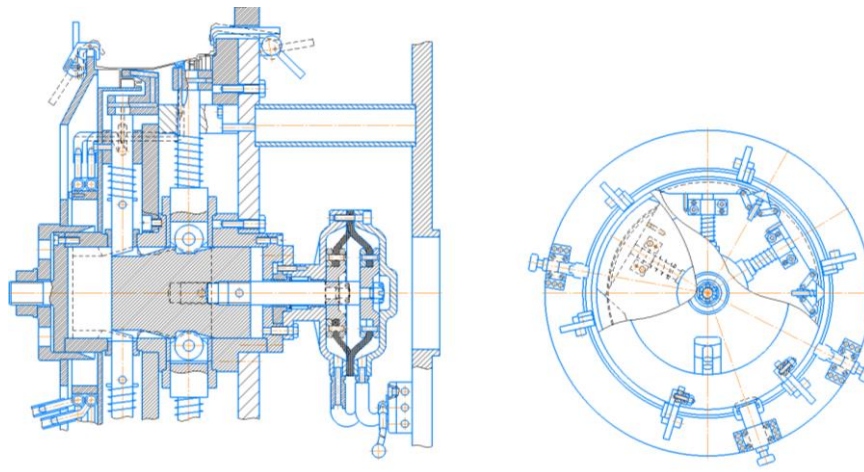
Приспособление П2 для сборки и сварки кольцевых швов
